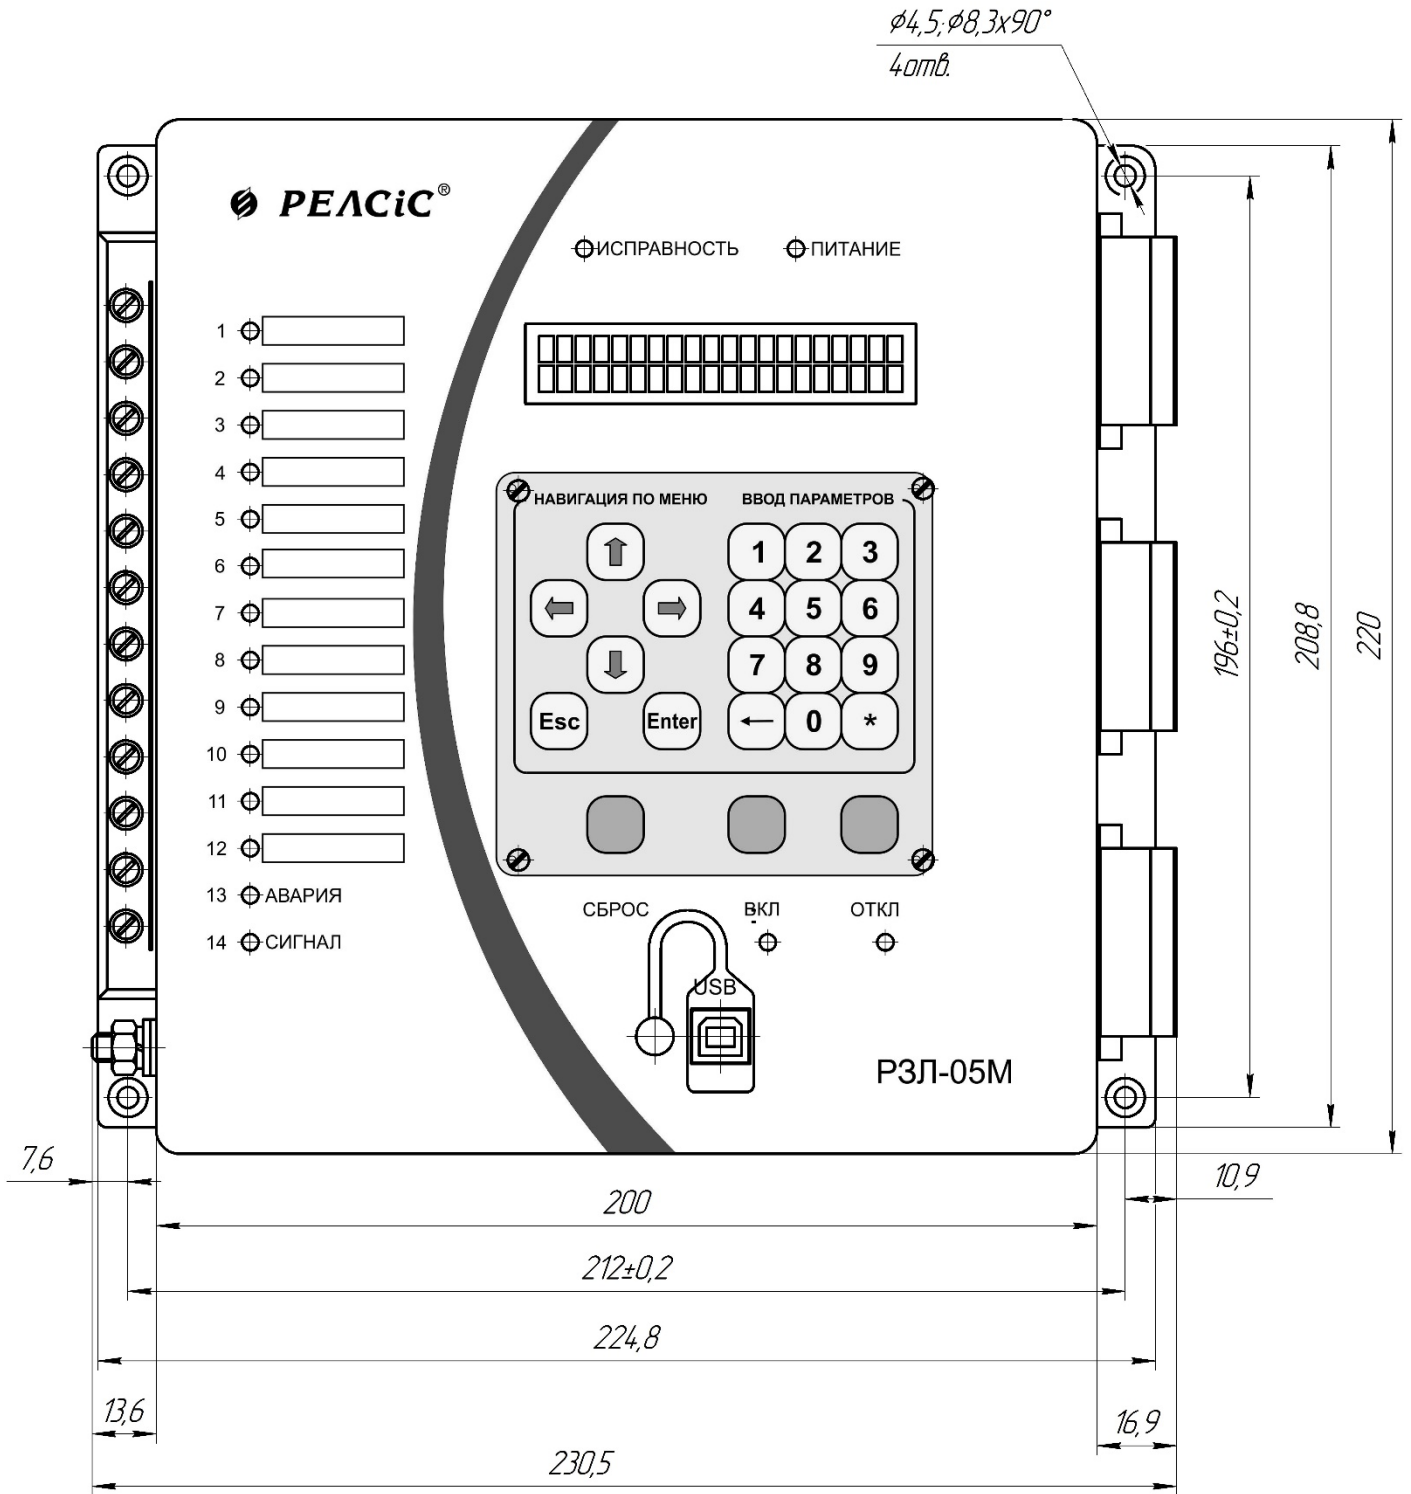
Габаритные размеры и установочные размеры и внешний вид передней панели устройства РЗЛ-05МХ-В
